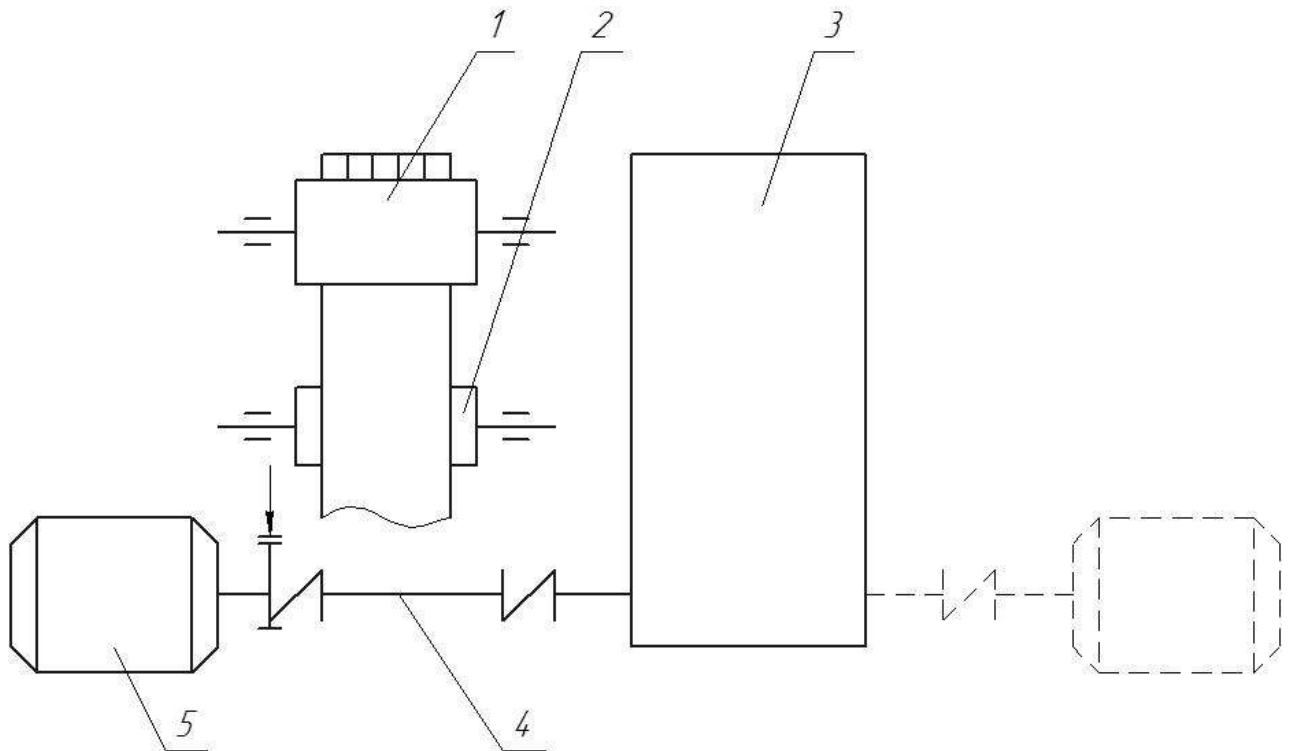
Схема приводу стрічкового конвеєра
